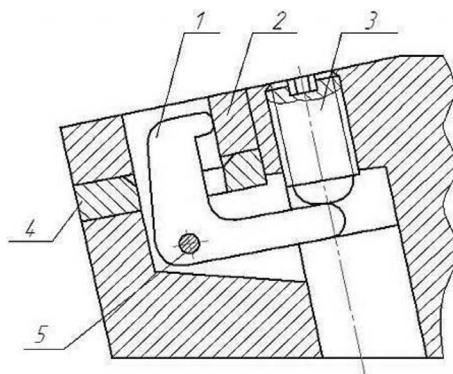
Крепление режущей пластины с помощью поворотного рычага
